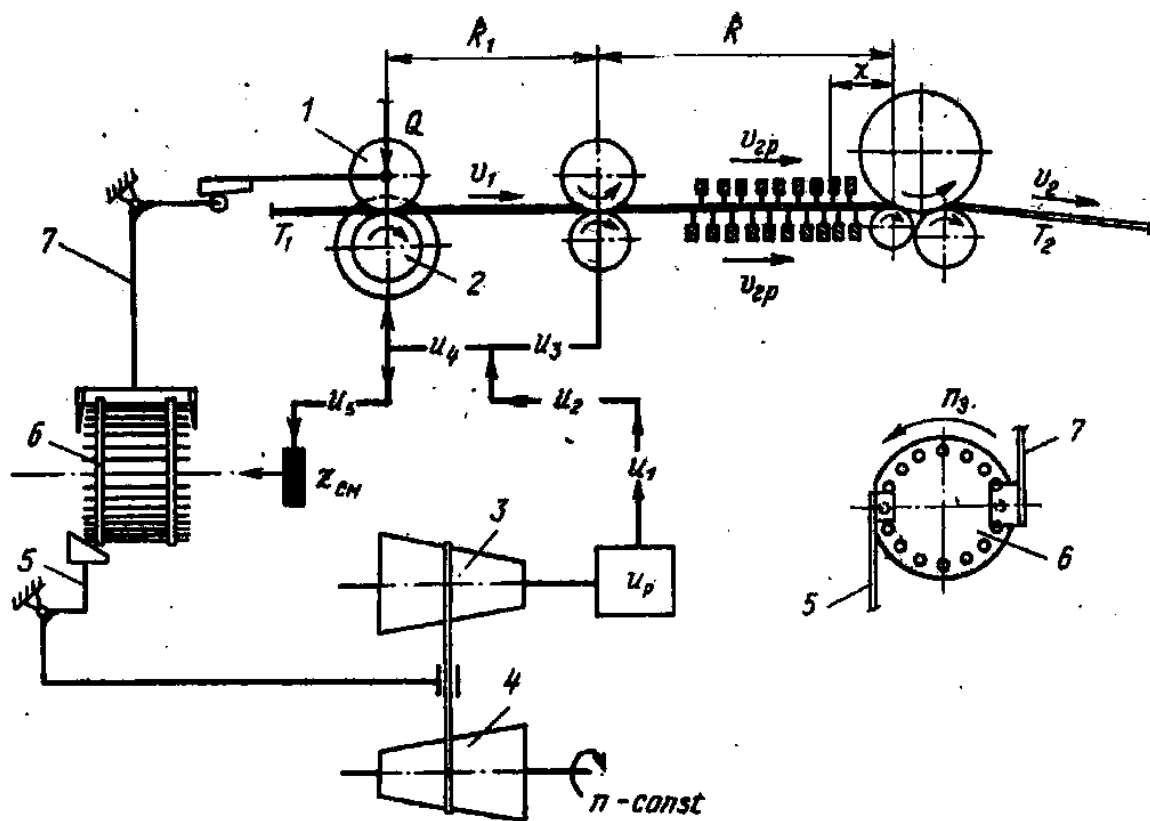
Технологічна схема автоматичного регулятора витяжки двопільної стрічкової машини
